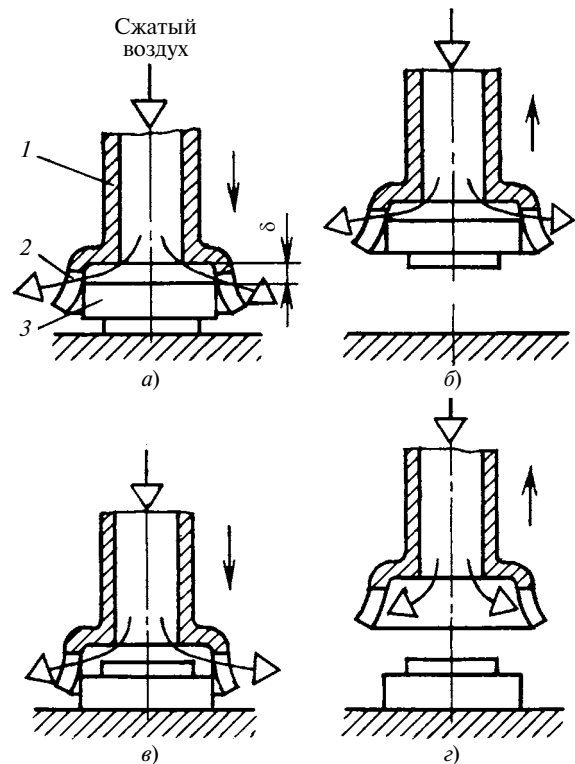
Схемы сортировки деталей с помощью струйного захвата *1*:
